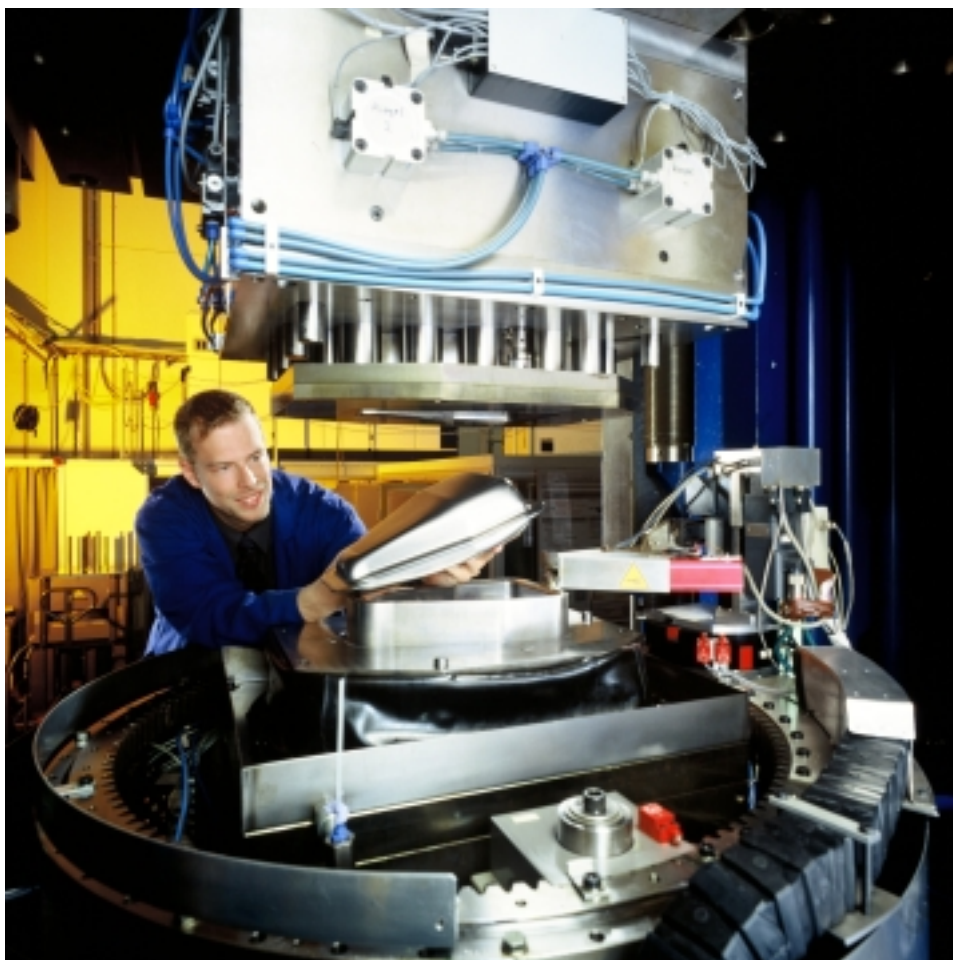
Umformwerkzeug mit integriertem Schweißroboter und hergestelltem Bauteil
